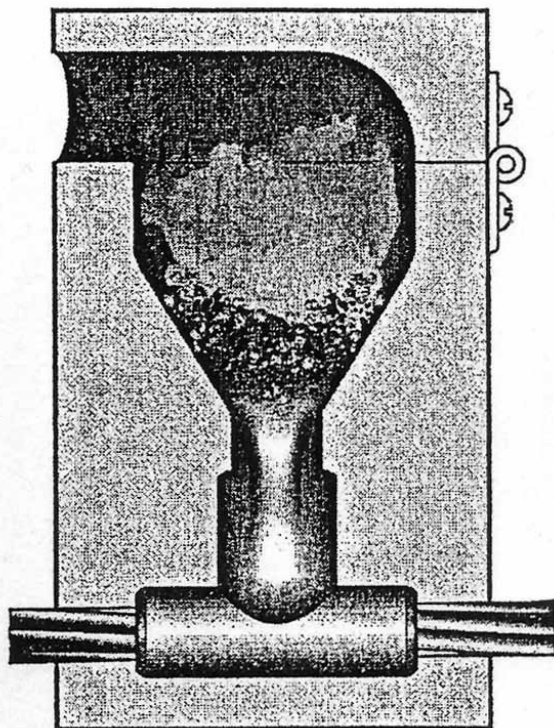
Fin de la colada y formación de la soldadura
